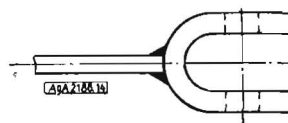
Gelenkgabel als Schmiedeteil oder Stahlgußteil, evtl. durch Brennschneiden hergestellt. Diese ist für Stumpfschweißung (Abbrennschweißung) besonders geeignet. Sie stellt schweißtechnisch und festigkeitsmäßig die beste Lösung dar
